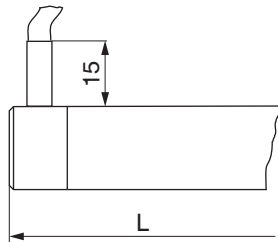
Wegsensor Typ - CR mit integriertem Kabel (radial)
